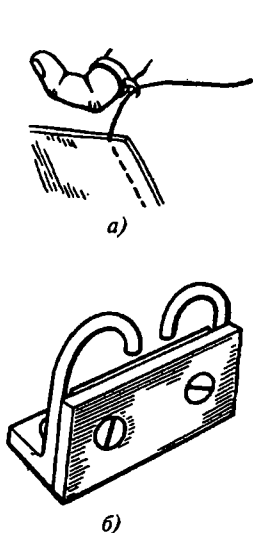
Кольцо с ножом (а) и стационарное приспособление для обрезки ниток (б)
